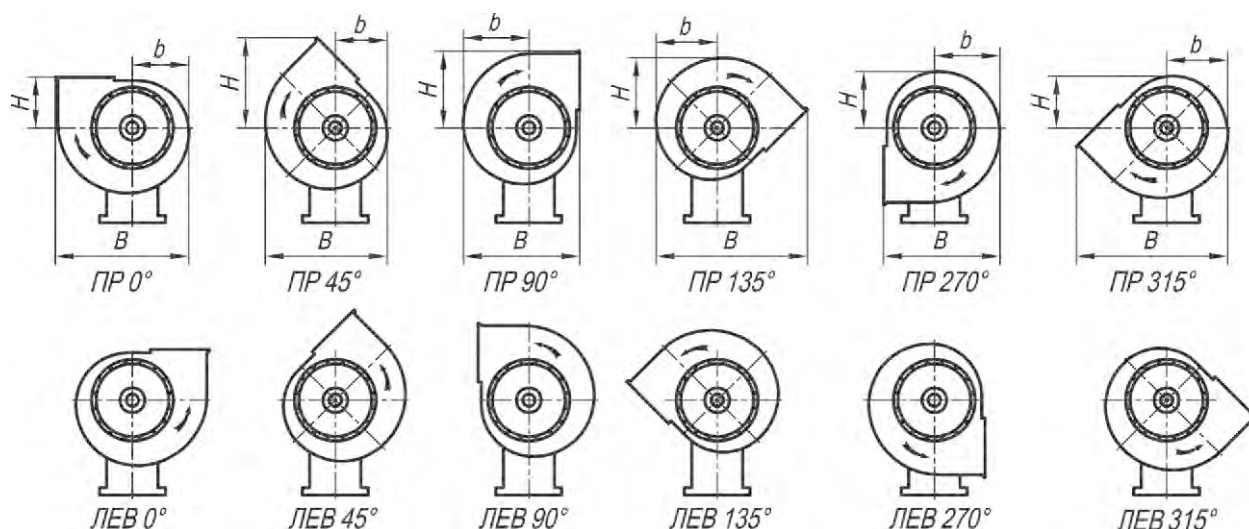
Положение корпуса вентилятора ВР 5-35, 5-45.
